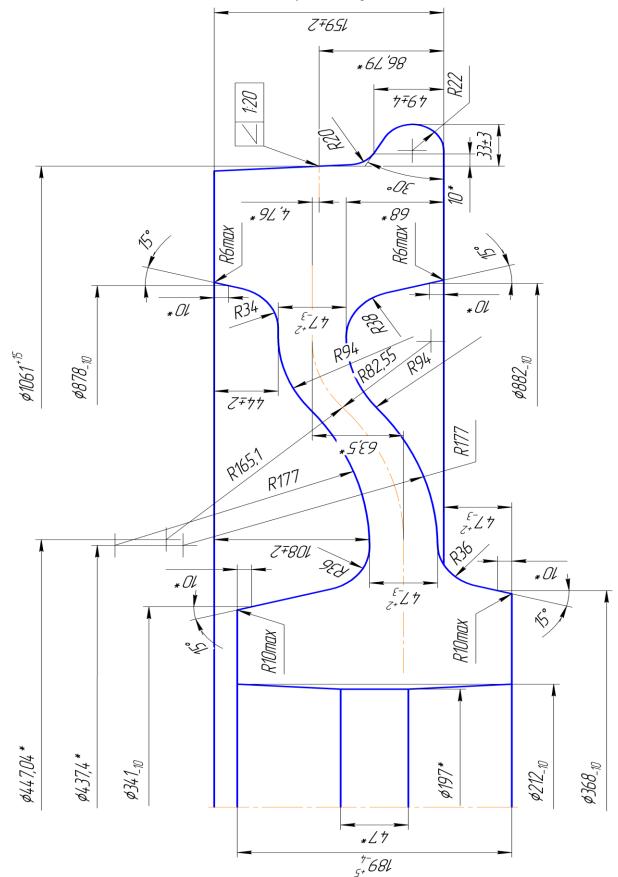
Колесо без механической обработки Ø 1061 мм. (под чистовое Ø 1046,16 черт. № КР-0091-12)
